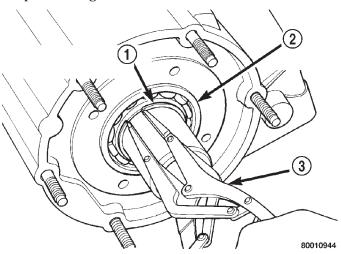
Desmontaje del anillo de retención del engranaje impulsor
